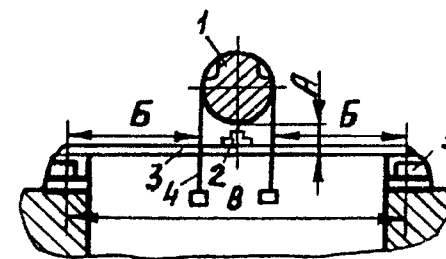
Выверка плит статора на фундаменте. 1-коленчатый вал; 2-уровень; 3- контрольная линейка; 4-отвес; 5- плита статора; А,Б,В- контрольные замеры
